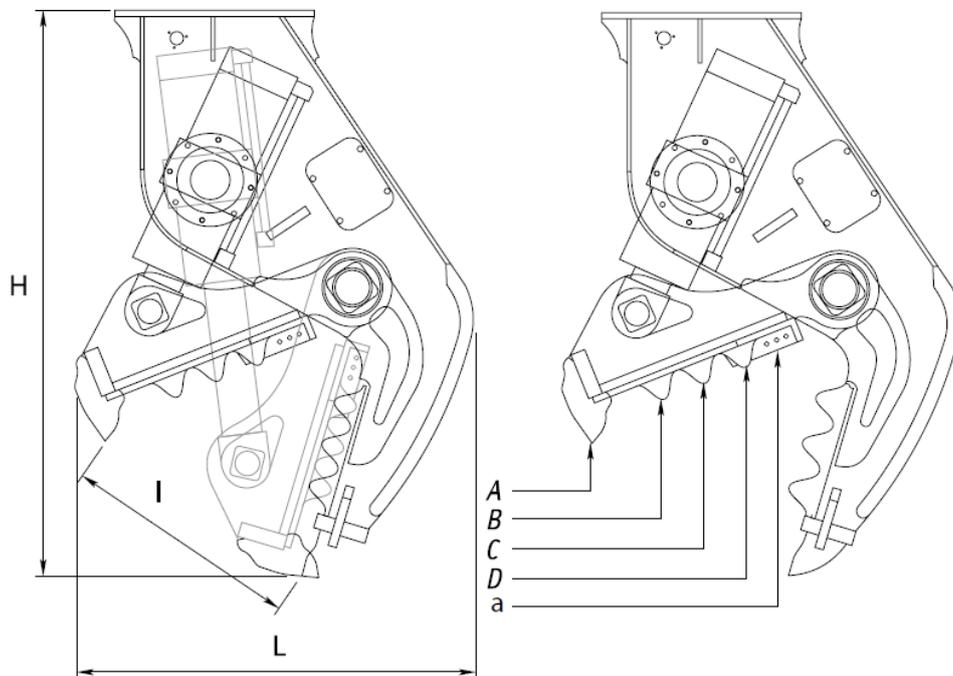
Конструктивная схема гидророжниц для измельчения бетонных конструкций
